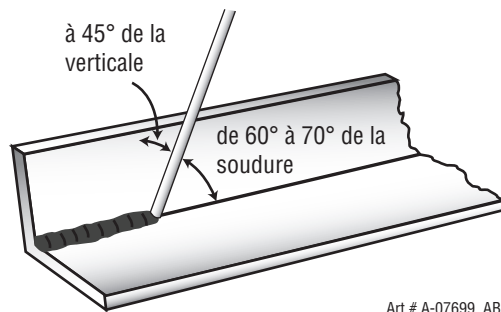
Position de l'électrode pour une soudure d'angle HV
